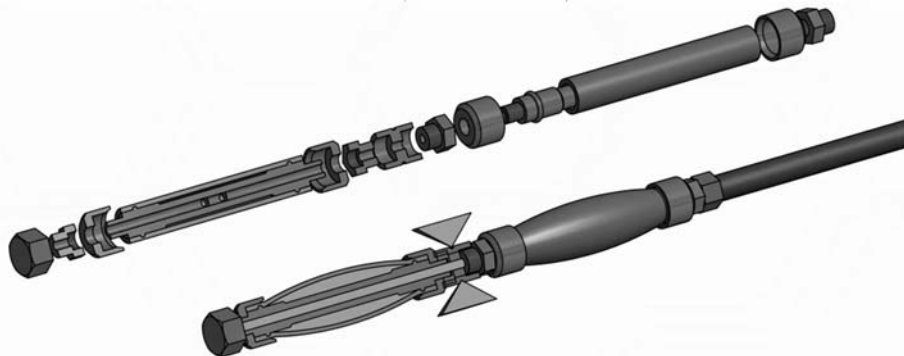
Конструкция и схема работы модернизированной конструкции пакера
